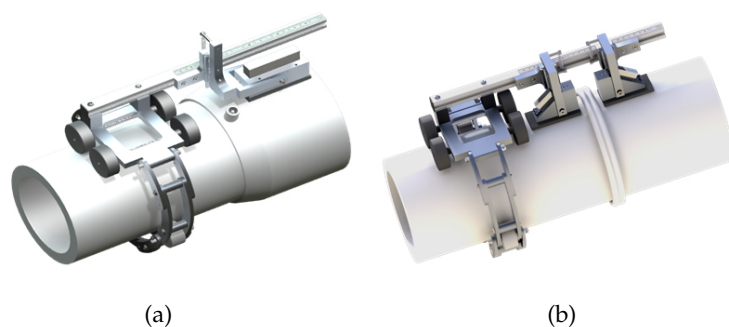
Configurations d'inspection usuelles pour les soudures PEHD. (a) Soudure EF inspectée en L0 avec un sabot droit rempli d'eau. (b) Soudure BF inspectée en mode TOFD avec une paire de sabots remplis d'eau et positionnés en vis-à-vis.
